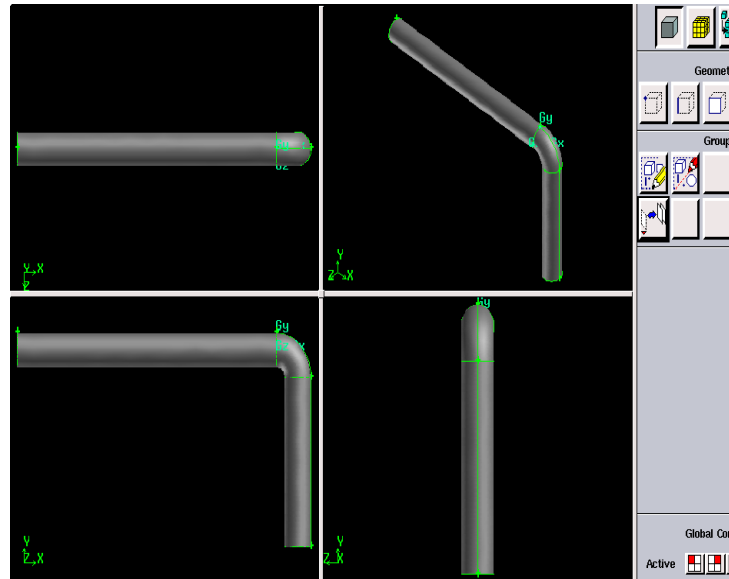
Dibujo en 3D del accesorio y extensiones de tubería
